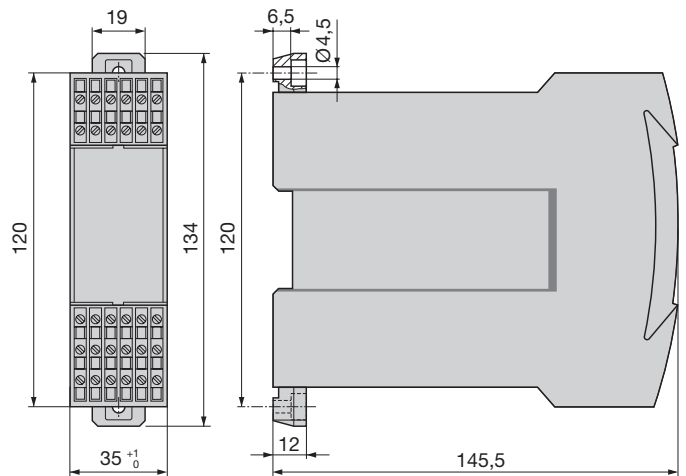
SINEAX VC 603 im Gehäuse S35 mit herausgezogenen Laschen für direkte Wandmontage.
